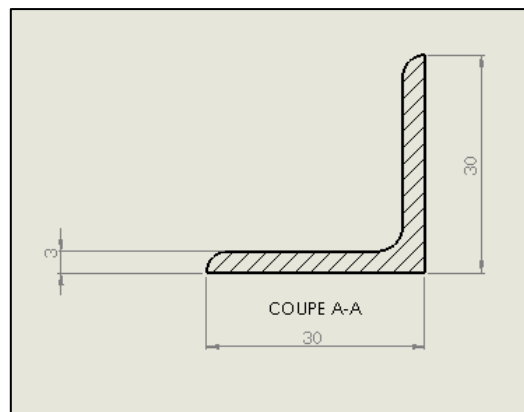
Vue en coupe de la cornière utilisée pour la structure de la machine
